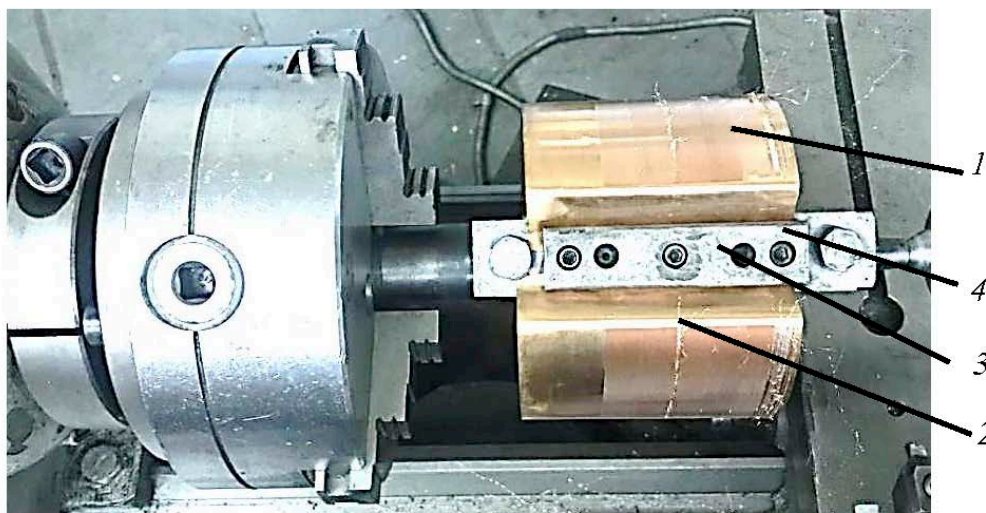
Общий вид приспособления с обрабатываемой полосой для получения капиллярной структуры на токарно-винторезном станке:
